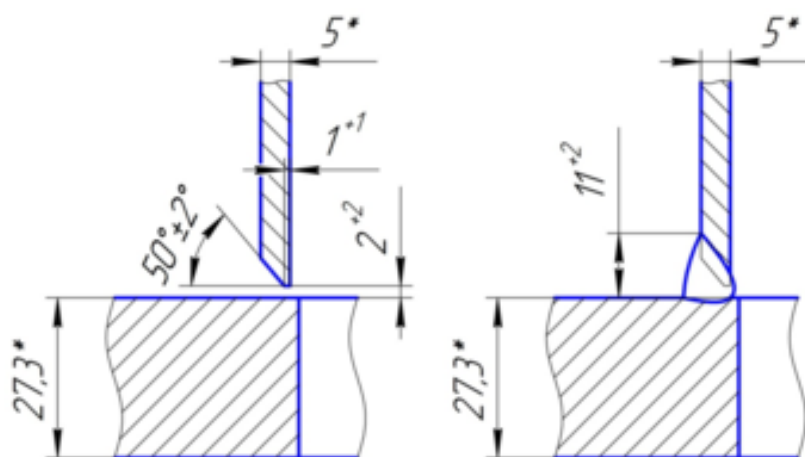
Общий вид сварного шва №1
